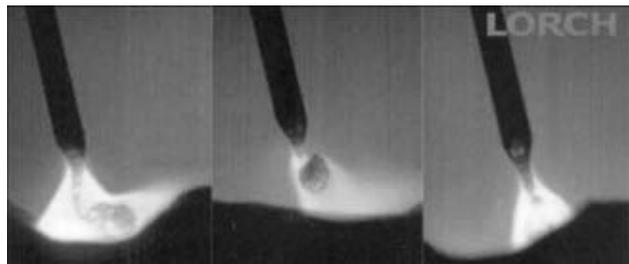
Сопоставление процессов сварки с режимами «Spray Arc», «Pulsed Arc» и «Speed Arc»
